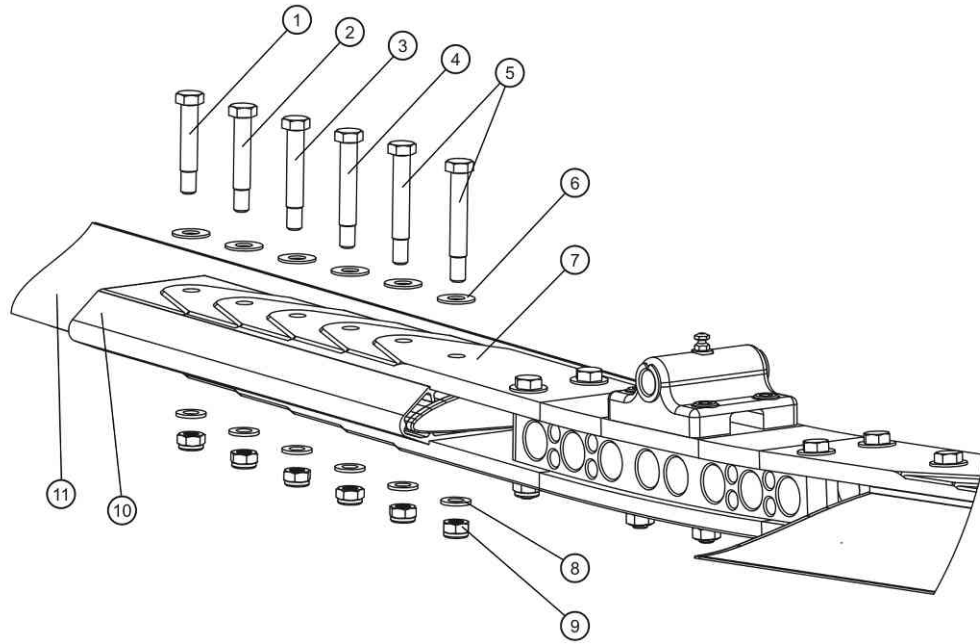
Zerlegen Rotor - schwenkgelagerte Teile
